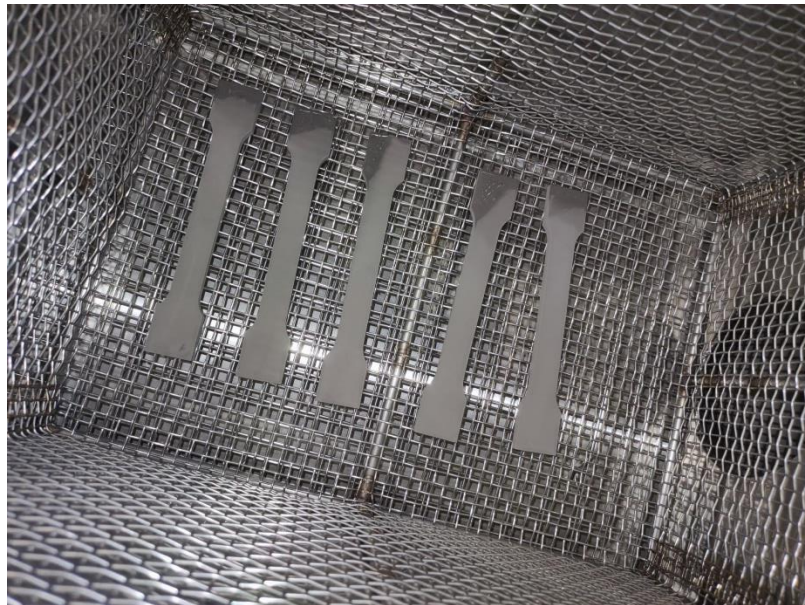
Colocación de las piezas verdes en la máquina de lavado Wash-1 [Fuente propia]
